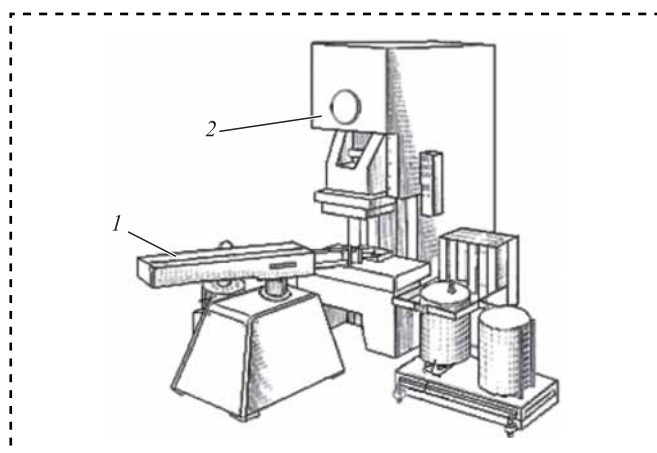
Станок для запрессовки втулок и осей в отверстия пластин ВРЦ: 1 — загрузочный робот; 2 — прессовое оборудование
